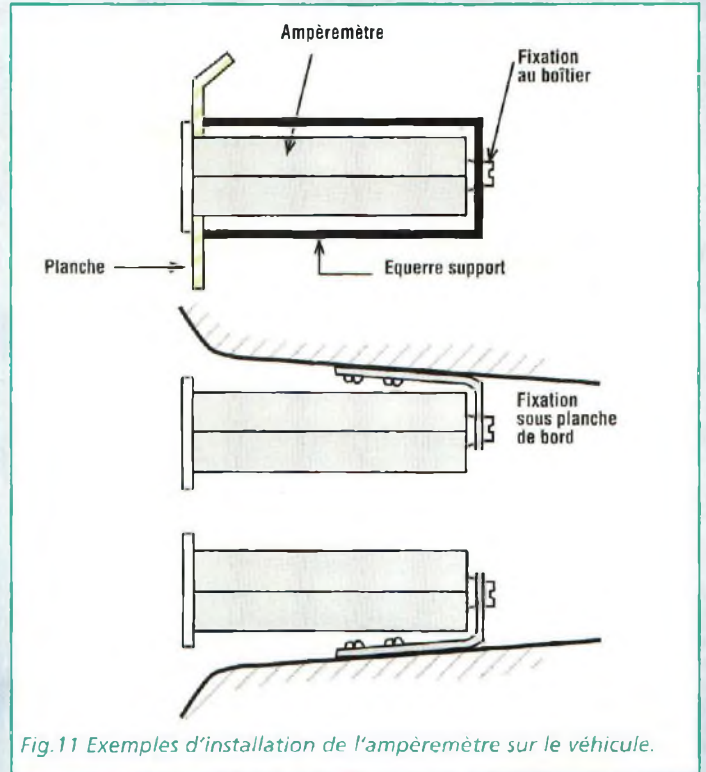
Exemples d'installation de l'ampèremètre sur le véhicule.
